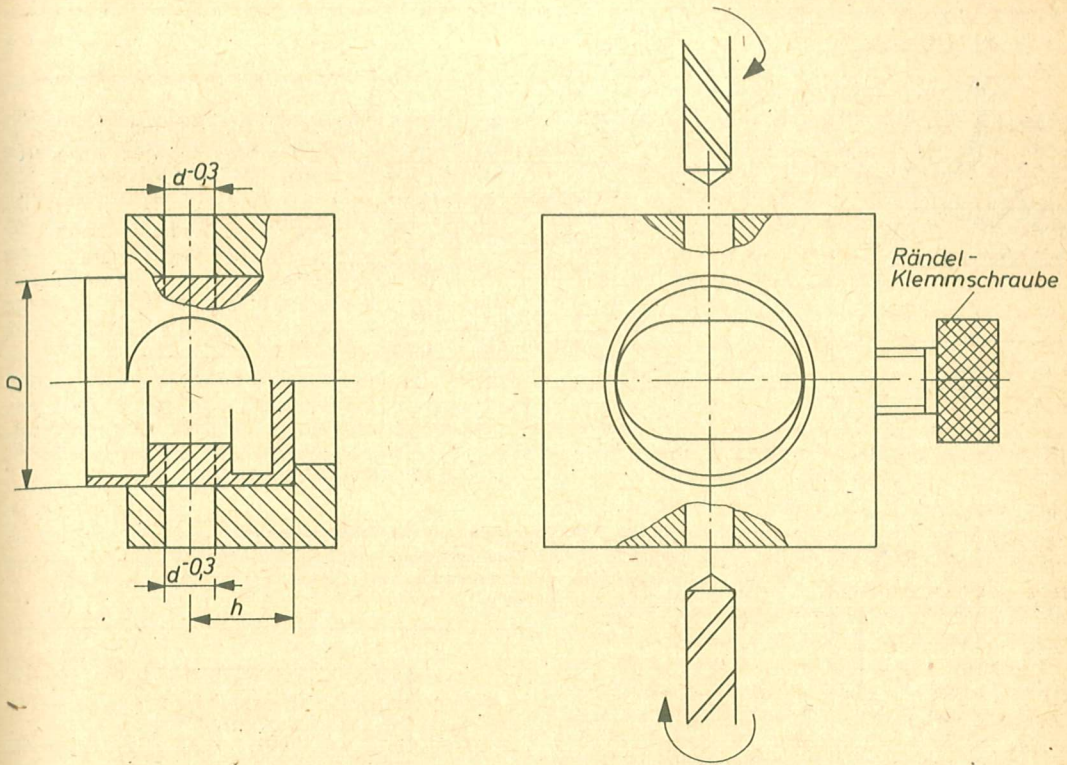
Bohrvorrichtung zum Bohren der Kolbenbolzenaugen. Wichtig ist, von beiden Seiten zu bohren, um ein Verlaufen des Bohrers auszuschließen. Nach dem Bohren wird mit einer Handreibahle die Kolbenbolzenbohrung gerieben. D und h je nach Kolben festlegen. $d-0,3$ mm unter Fertigmaß von beiden Seiten bohren ohne Kolben umzuspannen, dann Kolben ausspannen und von Hand auf Fertigmaß reiben.
